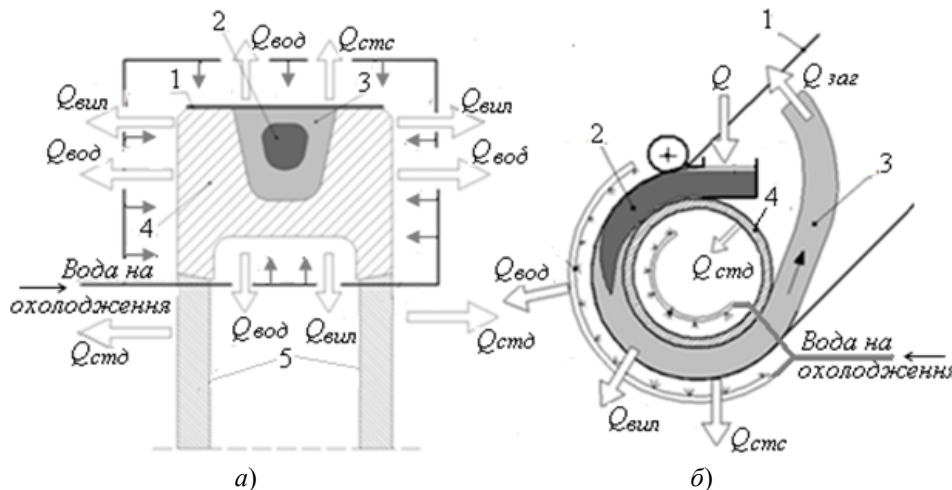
Поперечний (а) і поздовжній (б) переріз ливарного колеса та схема матеріальних і теплових потоків: 1 - сталава стрічка; 2 - рідка фаза заготовки; 3 - тверда фаза заготовки; 4 - виливниця кристалізатора; 5 - сталеві диски ливарного колеса
